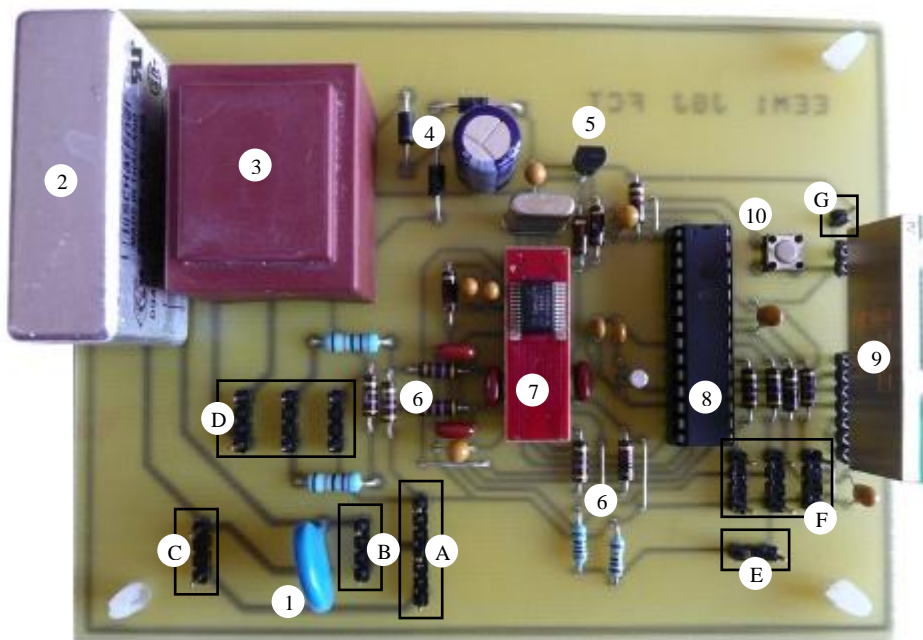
Componentes soldados na PCB do dispositivo de aquisição de dados
